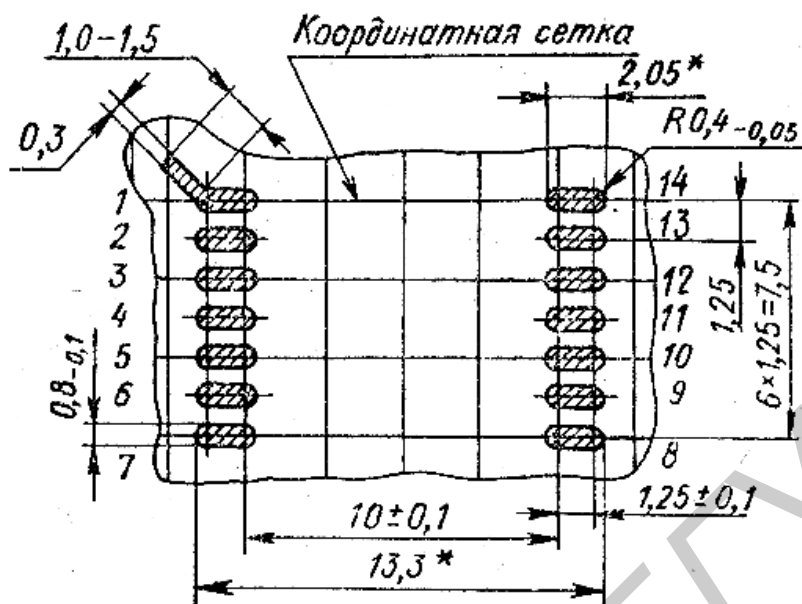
Разметка посадочного места для микросхем в корпусах типа 4 с овальными контактными площадками:
